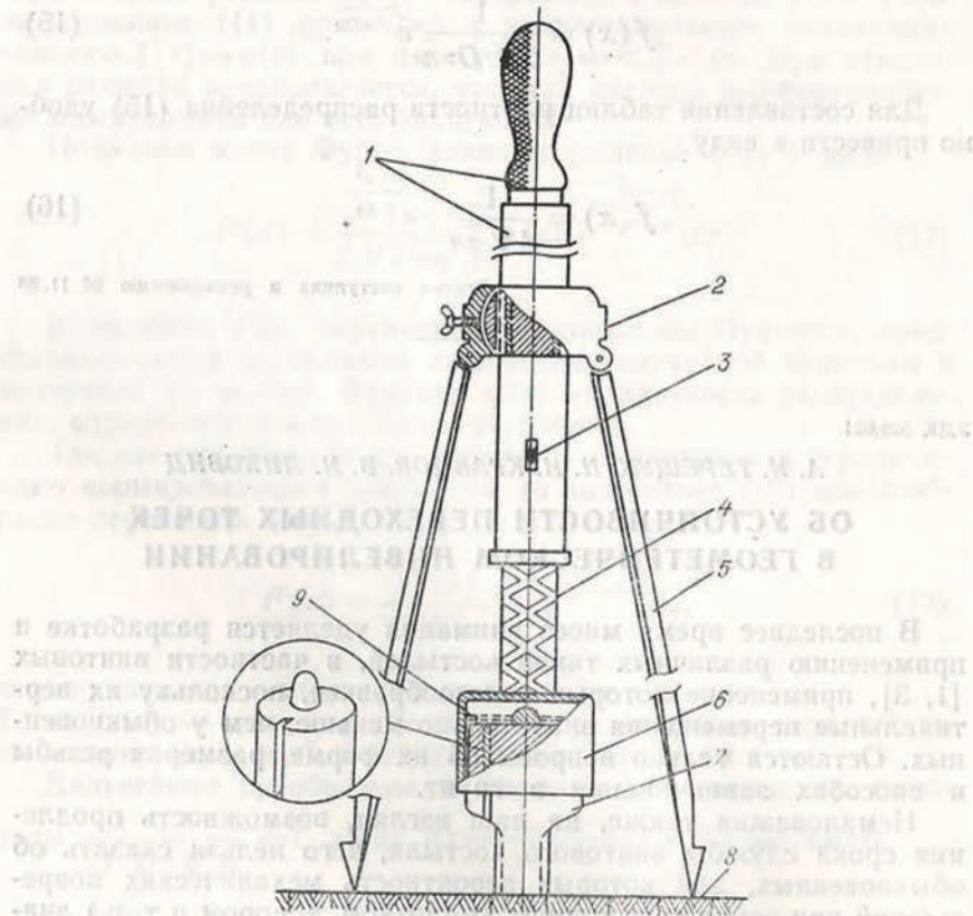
Приспособление для завинчивания (вывинчивания) резьбовых костылей.
